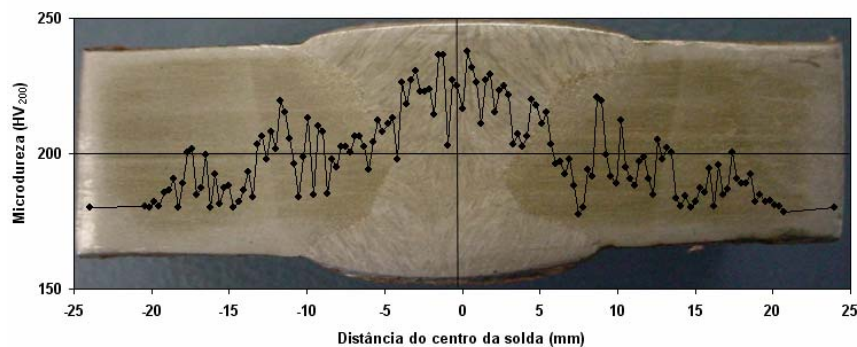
Perfil de dureza da junta soldada estudada.
